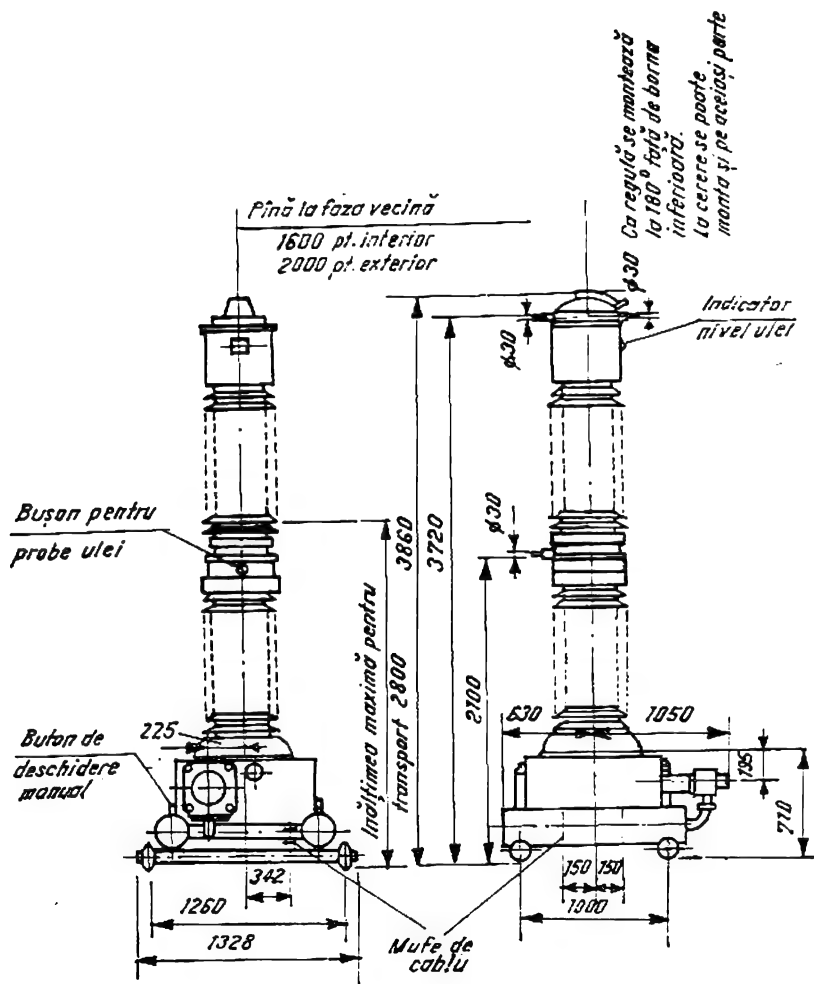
Întreruptoare IUP-110/1250 I, E cu acționare pneumatică. Dimensiuni de gabarit.
